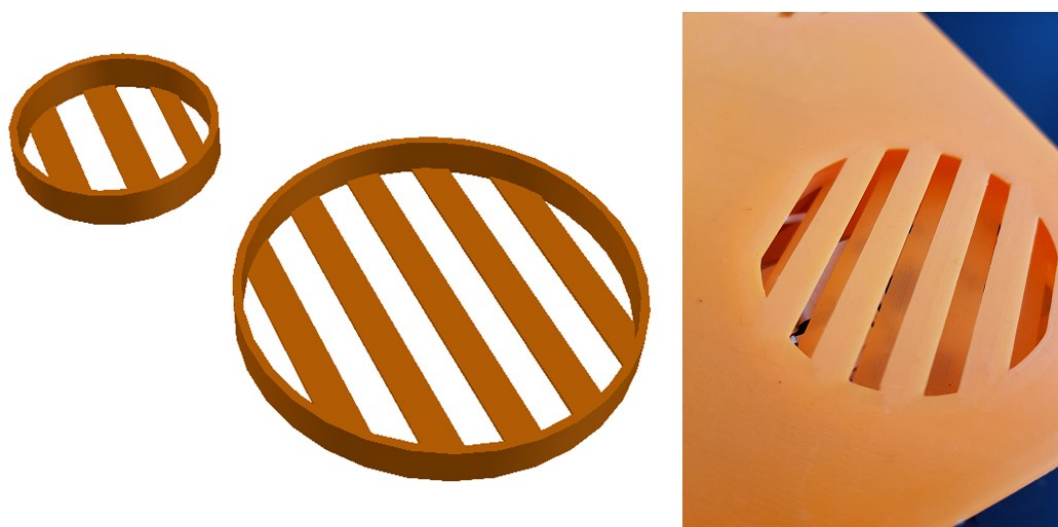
3D vizualizace a finální podoba střední části krytu
